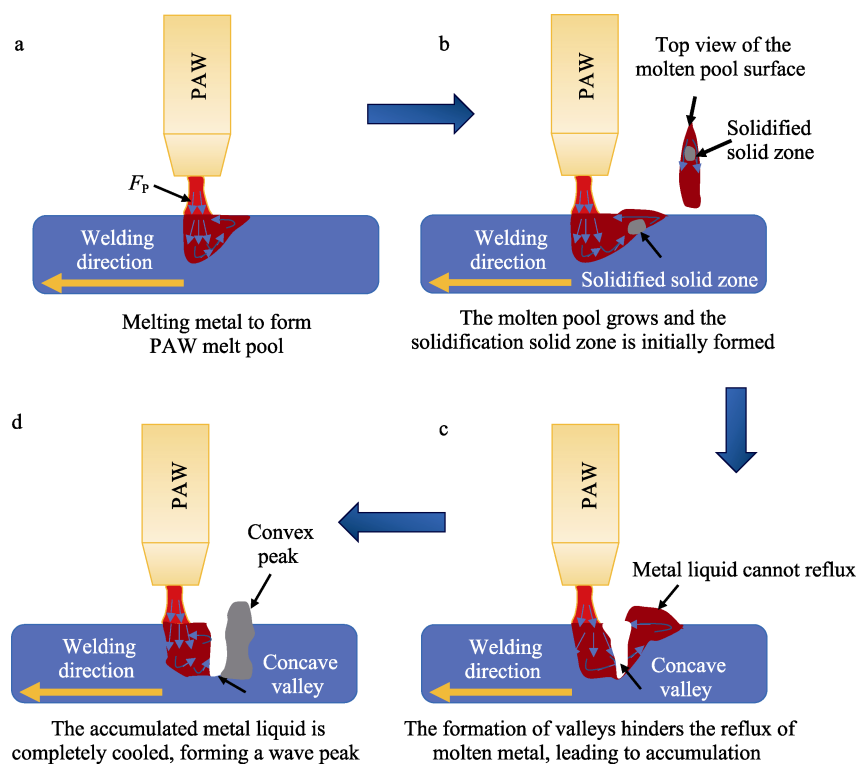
PAW 焊接过程中表面缺陷形成示意图
